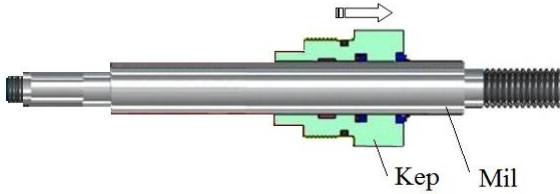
Önerilen otomatik montaj hüresinde iş akışı
